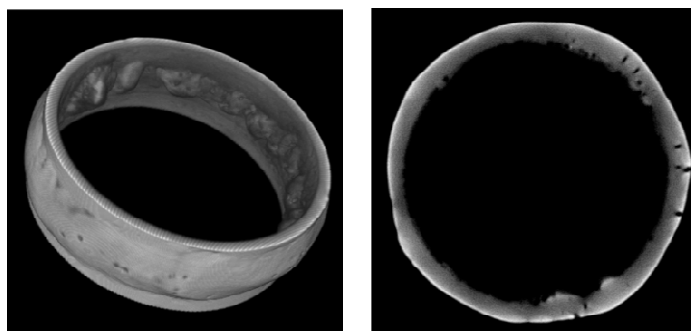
Трехмерная визуализация сварного соединения (слева), сечение исследуемого сварного шва (справа)
